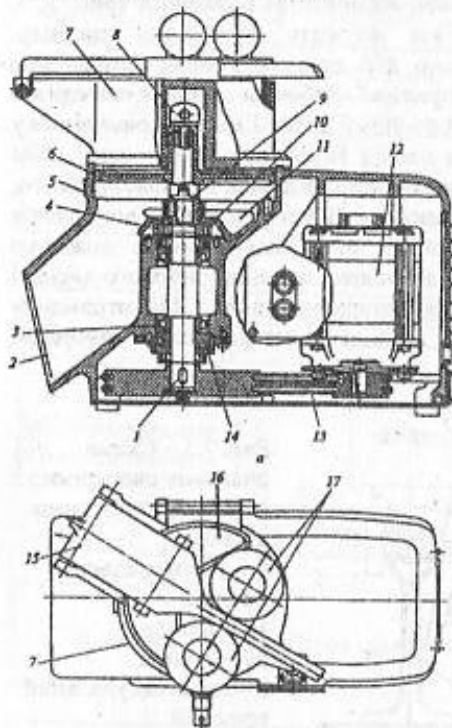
Універсальна овочерізна машина МРО 50-200: 1 – приводний вал; 2 – розвантажувальний пристрій; 3 – вальниці; 4 – гвинт; 5 – корпус; 6 – опорний диск; 7 – завантажувальний пристрій; 8 – гвинт; 9 – втулка; 10 – гайка; 11 – скидач; 12 – електродвигун; 13 – клинопасова передача; 14 – гайка; 15 – кронштейн; 16 – серповидний отвір; 17 – круглі отвори
